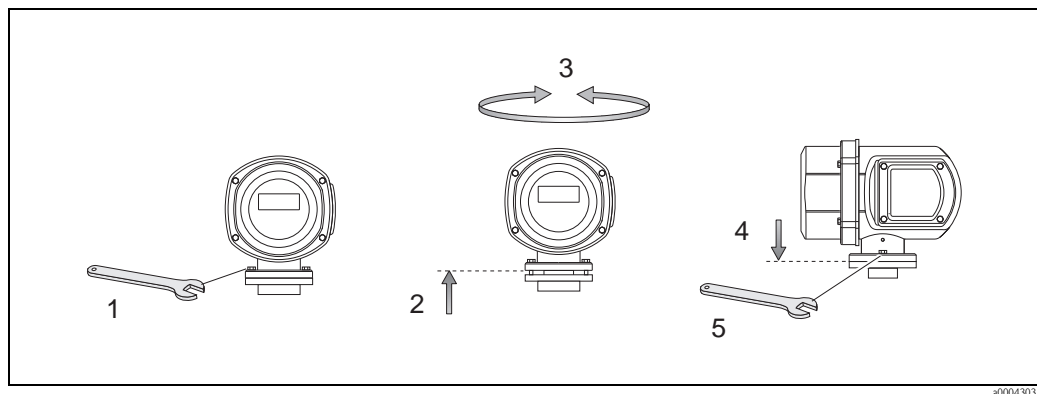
Drehen des Messumformergehäuses (Edelstahl-Feldgehäuse)
